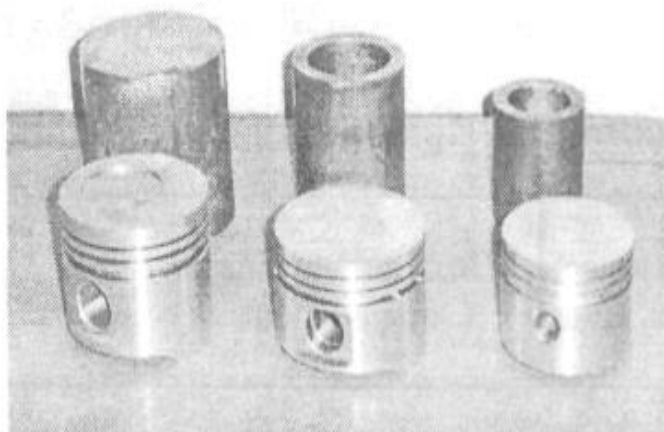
Заготовки та виготовлені з них поршні двигуна внутрішнього згорання
